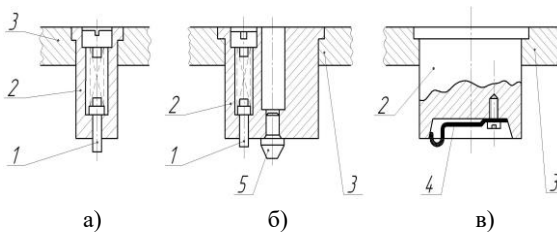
Примеры конструкции отлипателей: а – штырьевой отлипател, расположенный в центре пуансона; б – штырьевой отлипател, расположенный сбоку пуансона; в – отлипател в виде ленточной пружины; 1 – штырьевой отлипател; 2 – пуансон; 3 – пуансонодержатель; 4 – пружинный отлипател; 5 – ловитель
